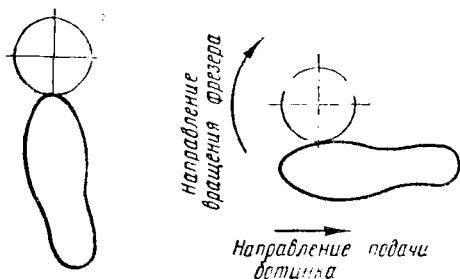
Положение фрезеруемой обуви по отношению к фрезеру
